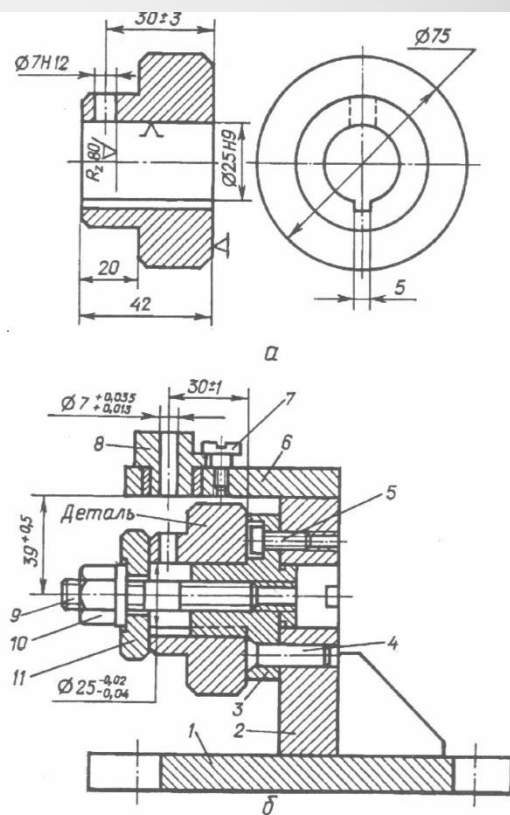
Кондуктор зварної конструкції для радіального свердління отвору в деталі “муфта”:
